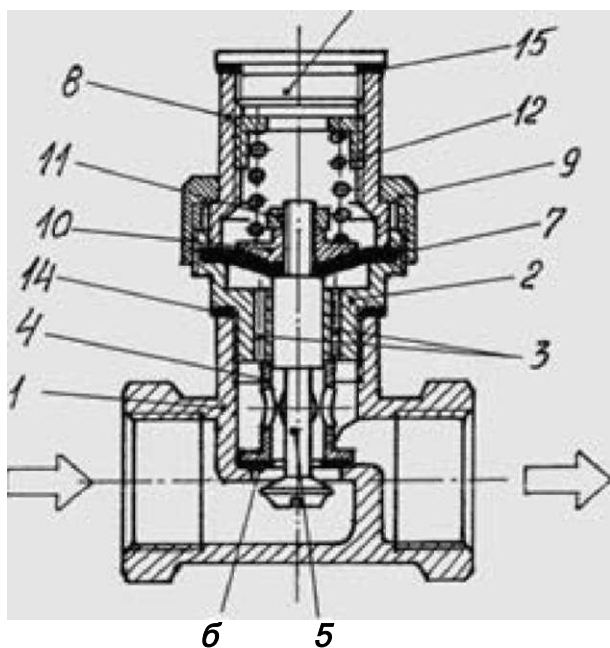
Принципиально-конструктивная схема клапана РДВ 15-2А-М (1 — корпус; 2 — стакан; 3 — дросселирующие каналы демпфера; 4 — втулка; 5 — шток с жестким клапаном; 6 — эластичное седло клапана; 7 — разделительная мембрана; 8 — регулировочный винт натяга пружины; 9 — накидная гайка; 10 — грибок; 11 — контргайка; 12 — крышка; 13 — заглушка; 14 и 15 — уплотнительные шайбы)
